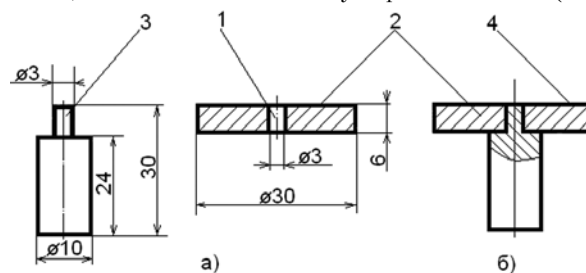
Образец для исследования прочности адгезии полимерных покрытий: а – геометрические размеры, б – образец в сборе
